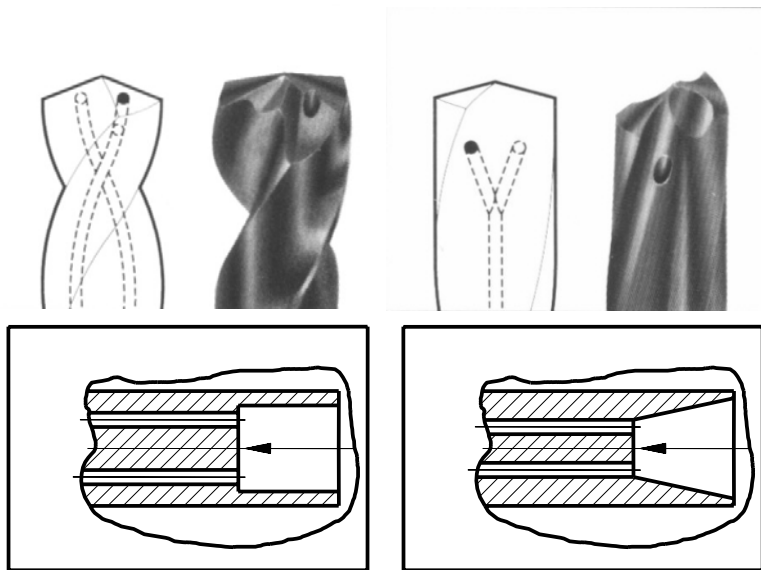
Ausführung des Bohrers, oben Schneiden und Spannuten, unten Schaft. Links ungünstig, rechts richtig
